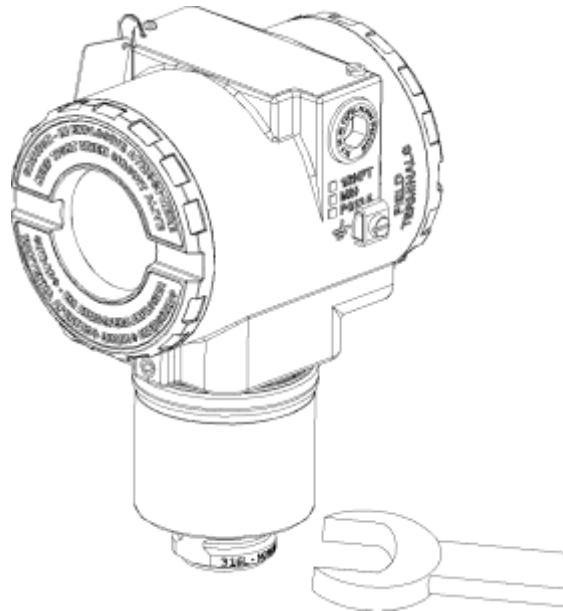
(c)– Desenho Dimensional e Posição de Montagem para o LD293 – Transmissor de Nível
